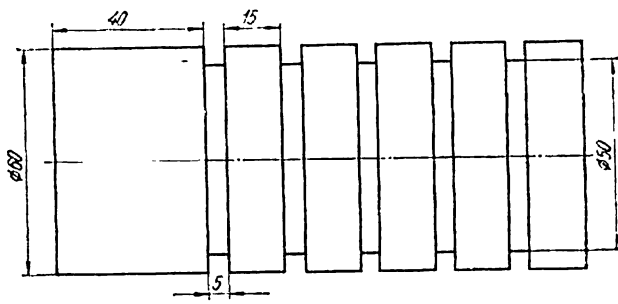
Образец для испытаний шероховатости обработанной поверхности.
